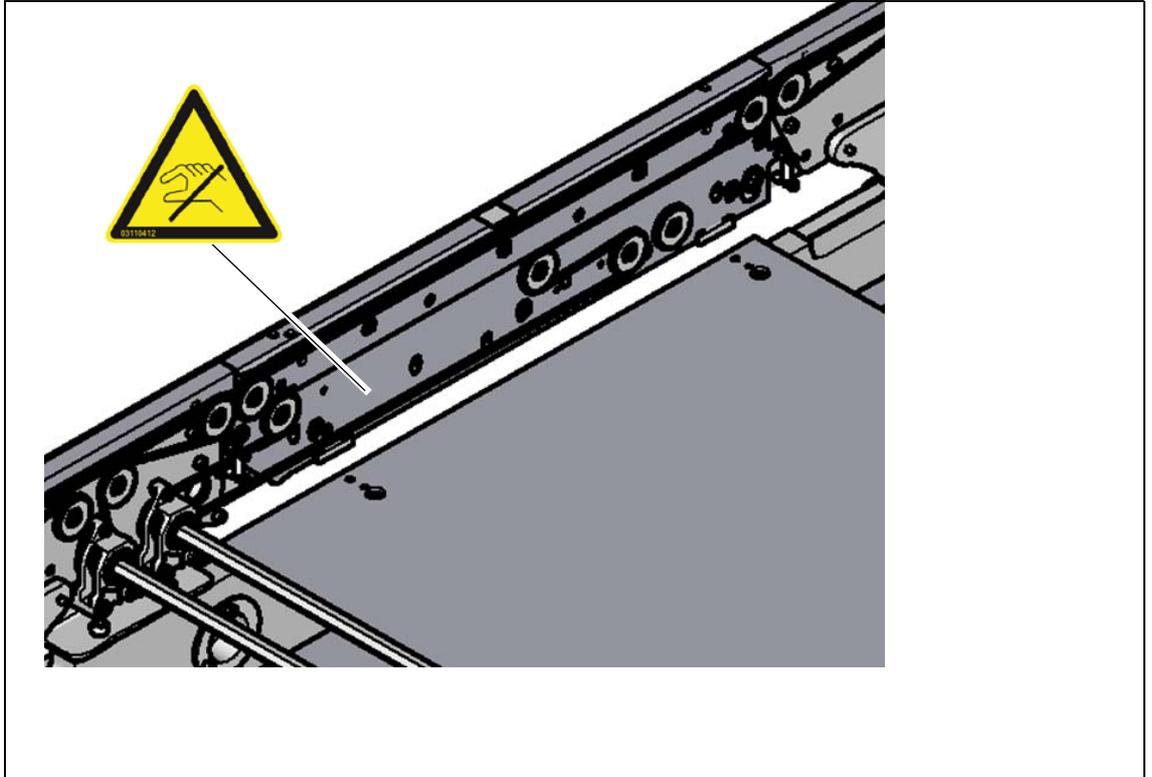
12 PCB 传送导轨夹板上的警告标签 "传送导轨侧面非常敏感"
